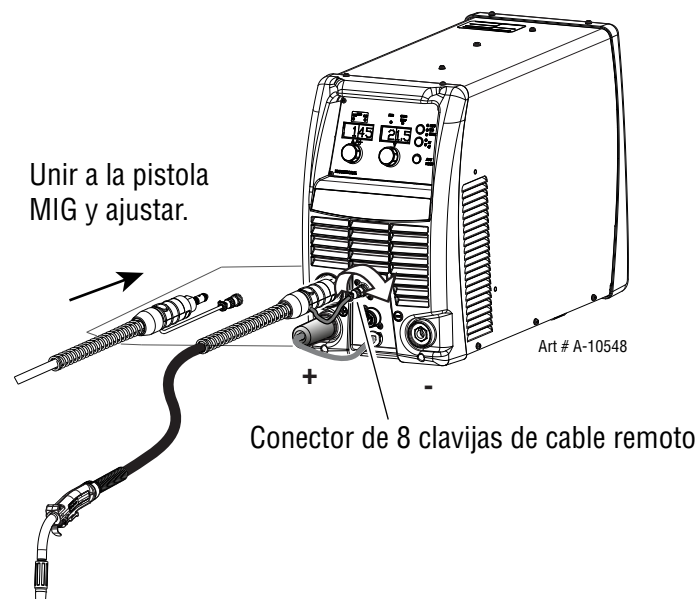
Montaje del cable de la pistola de MIG al receptáculo del adaptador
